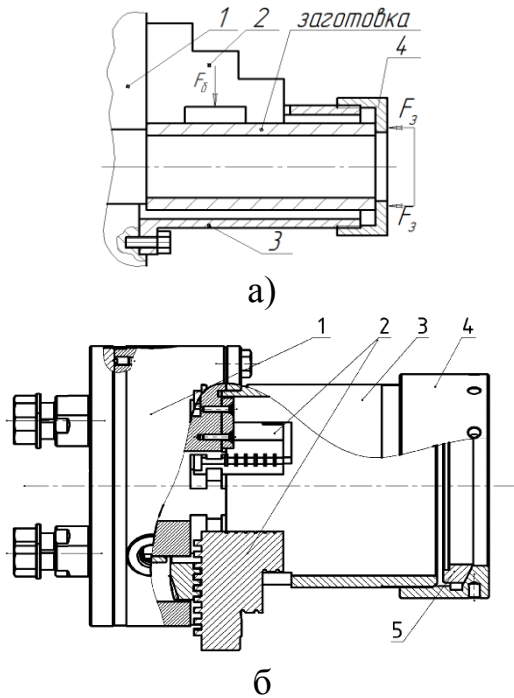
Розрахункова а) та конструктивна б) схема патрона для базування та затиску циліндрів з глибокими отворами: 1 – корпус; 2 – кулачки; 3 – фланець; 4 – затискна гайка; 5 – спеціальна шайба
